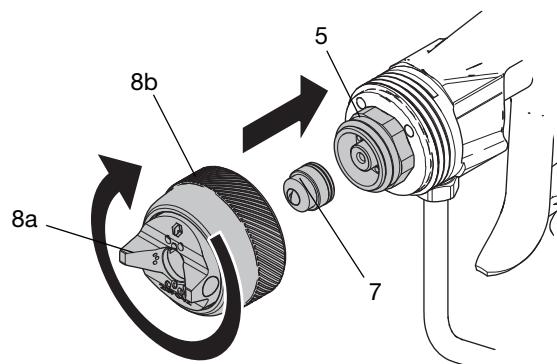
Установка сопла и воздушной головки (вид сзади)
